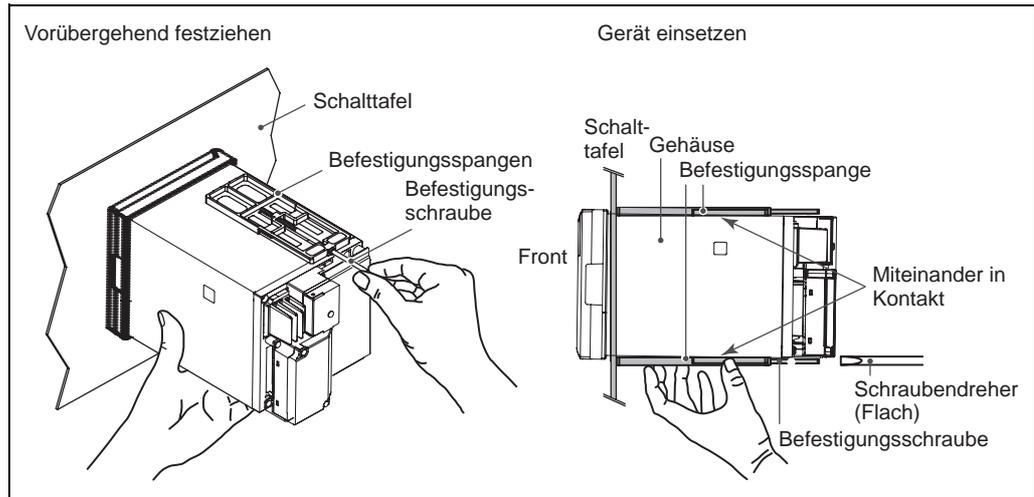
Schalttafelmontage - Gehäuse mit Befestigungsspannen auf der Ober- und Unterseite.
